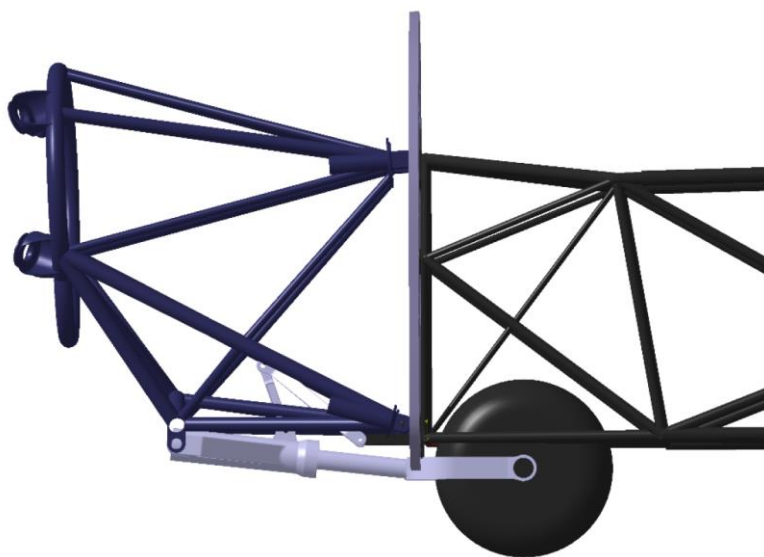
Aktuálne motorové lôže Z 143 [5]
